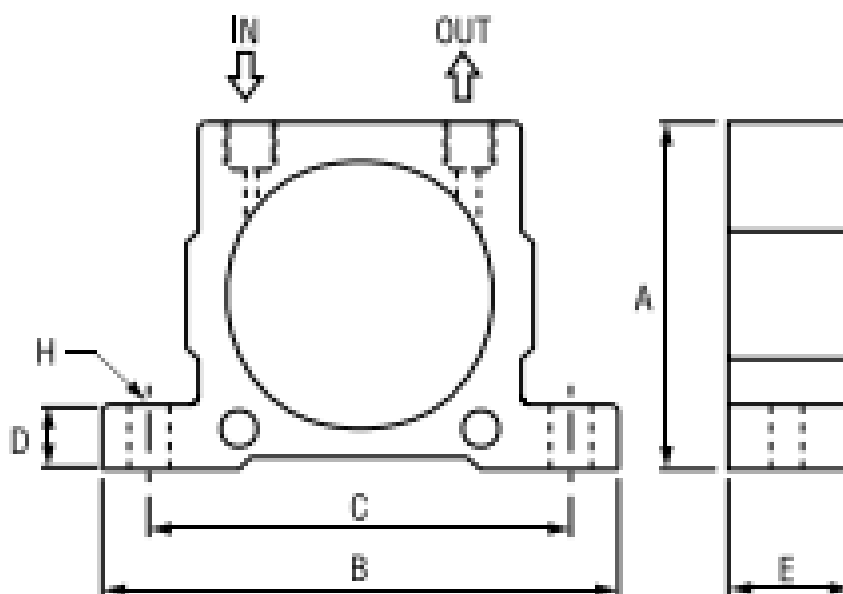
Загальні розміри пневматичного кулькового вібратора.
